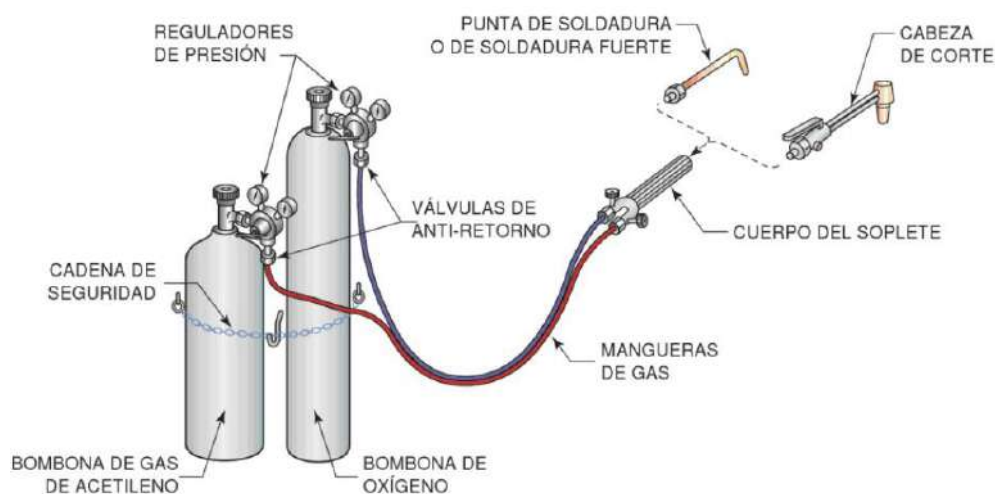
esquema de soldadura OAW, fuente: "Ingedemy" (Facebook)
